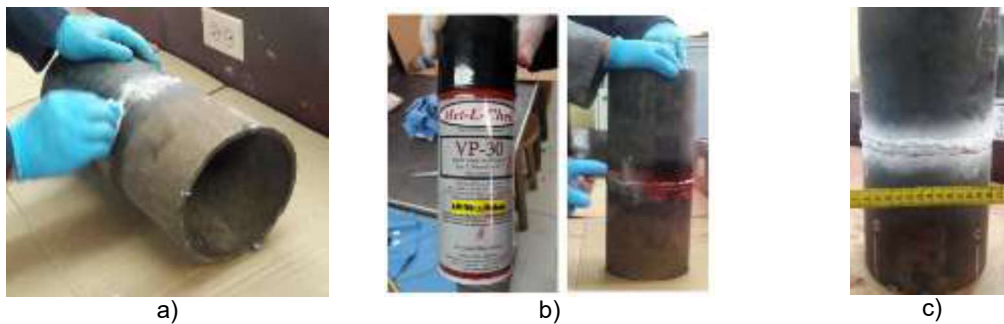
Tintas penetrantes. a) Limpieza de Probeta. b) Aplicación de penetrante. c) Inspección.
